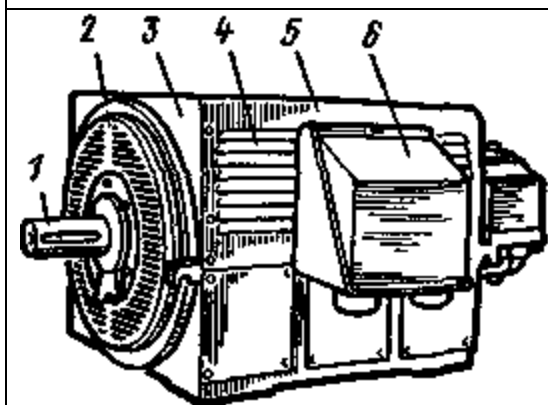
Асинхронный двигатель каплезащищенного исполнения (степень защиты IP23): 1 — вал; 2, 4 — вентиляционные окна для входа и выхода охлаждающего воздуха; 3 — подшипниковый щит; 5 — станина; 6 — коробка с выводами
